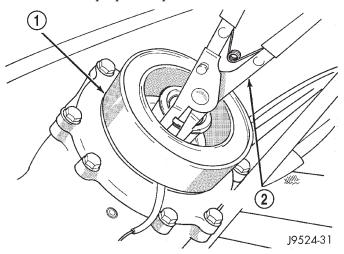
DESMONTAJE DE ANILLO DE MUELLE DE BOBINA DE CAMPO DE EMBRAGUE - característico
